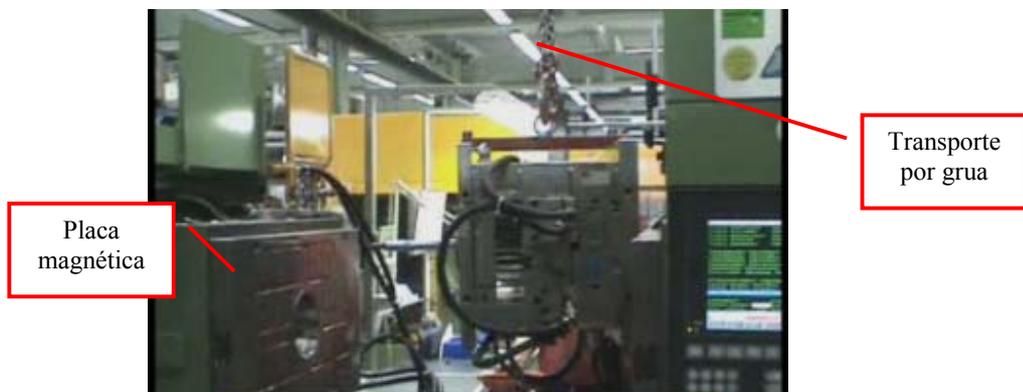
Placa magnética que fixa moldes e transporte por grua.
